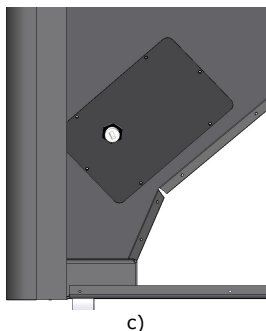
Colocação do sensor de nível de *pellets* no silo (instalação do silo à esquerda da caldeira)
